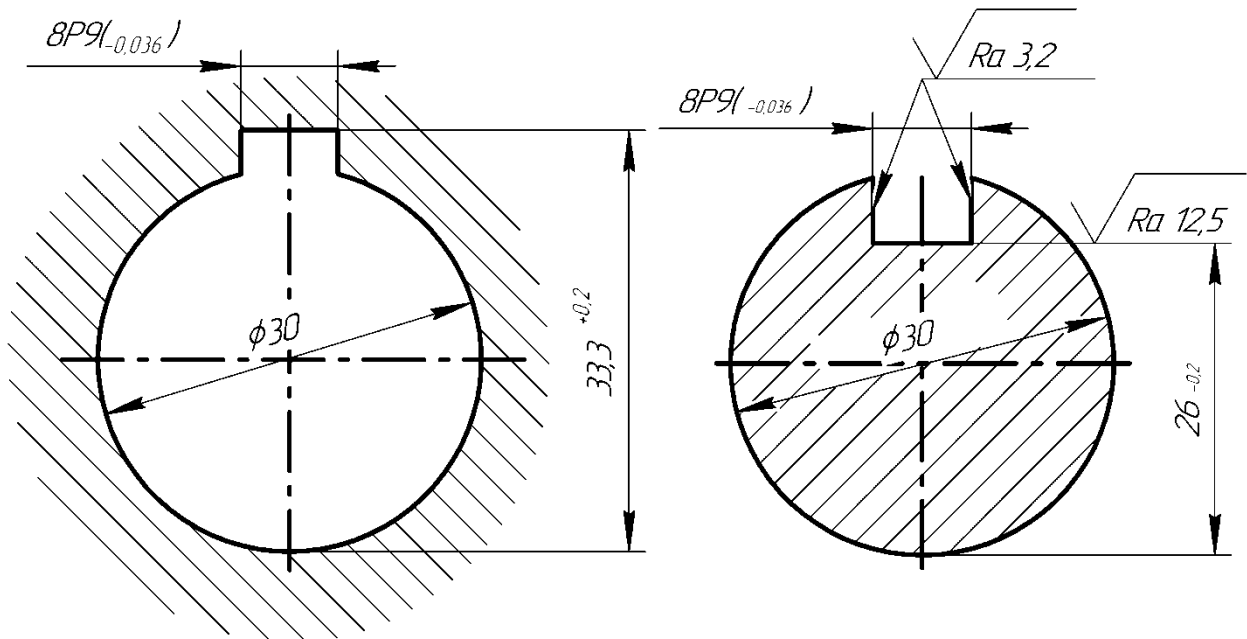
Обозначение допусков шпоночного соединения по ширине на детализовочных чертежах
